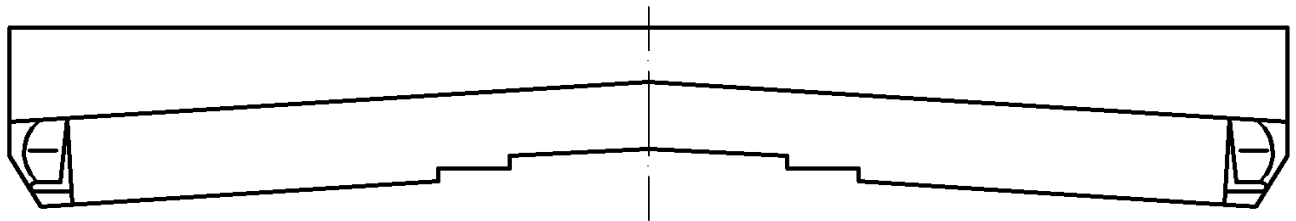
шеврон ніж зі складною формою ріжучої кромки конструкції «НКМЗ» [53]
